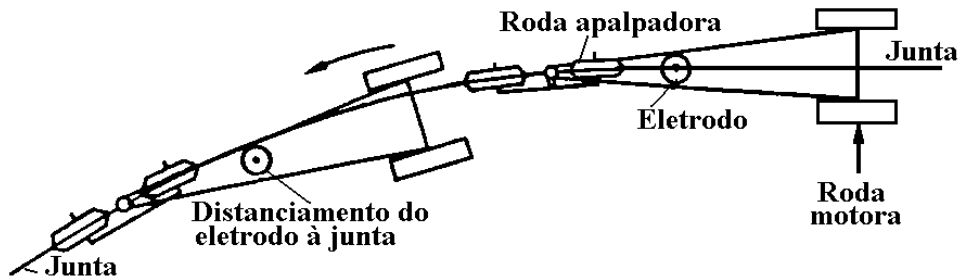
deslocamento de soldagem guiado por seguidor mecânico circular, tipo não-articulado.
